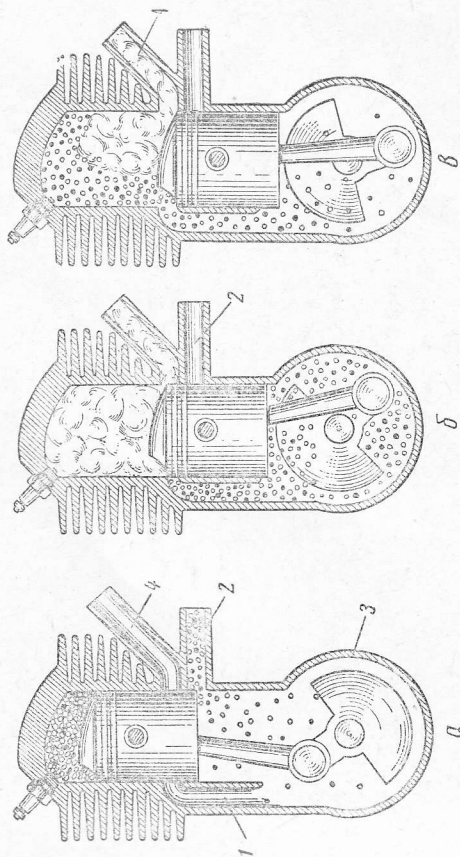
Двухтактный рабочий цикл карбюраторного двигателя:
